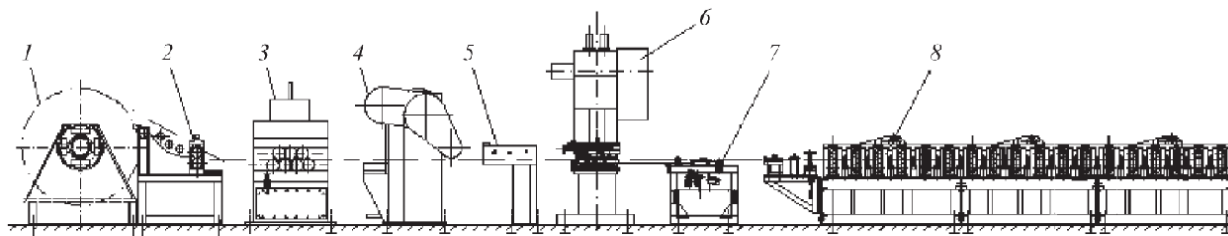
Профилировочная линия с расширенными технологическими возможностями: 1 – разматывающая рулонница; 2 – тянущее устройство с отгибателем кромок; 3 – правильная машина; 4 – пресс для подрезки заготовки; 5 – подающее устройство; 6 – перфорирующий пресс; 7 – синхронизирующее устройство; 8 – профилировочный стан
